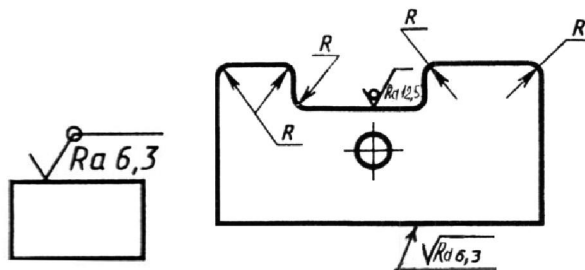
Обозначение шероховатости поверхности детали по контуру
